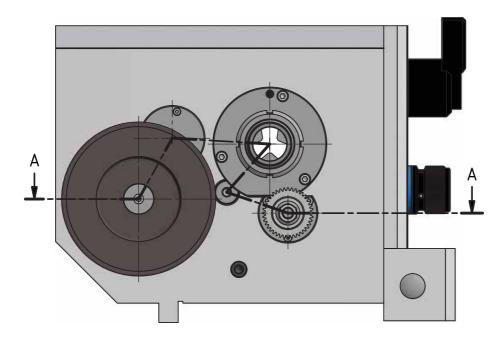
Getriebe Spindelstock 1-6 - Headstock gear 1-6
